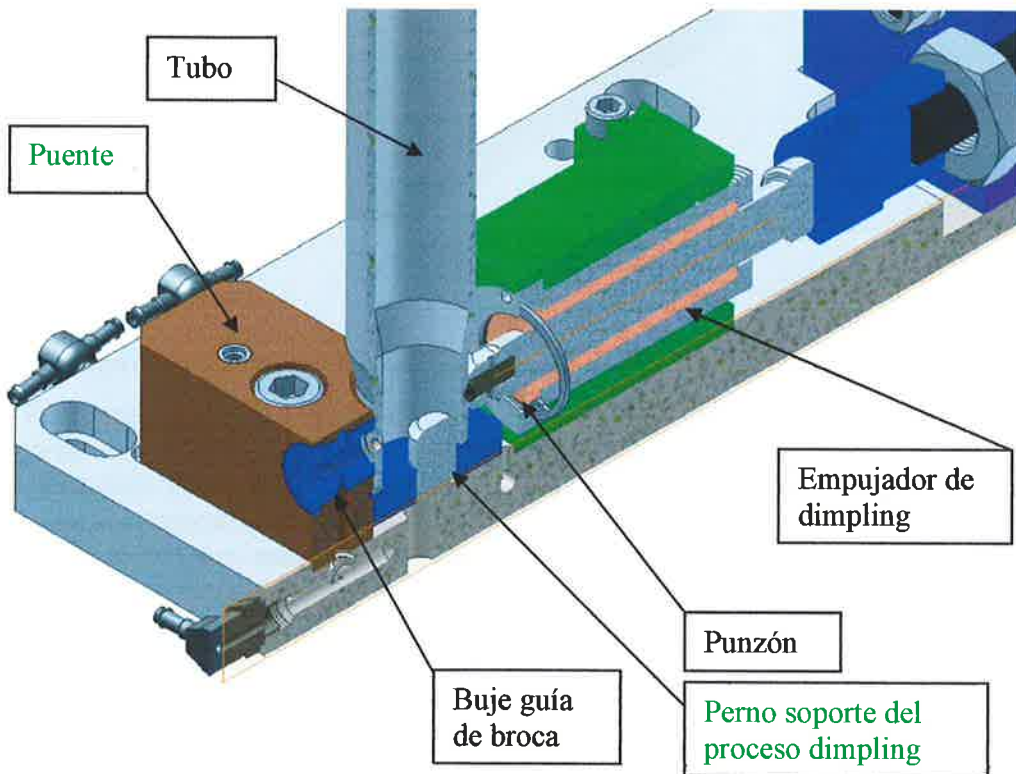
Dibujo con corte de partes principales del Sistema Dimpling.
